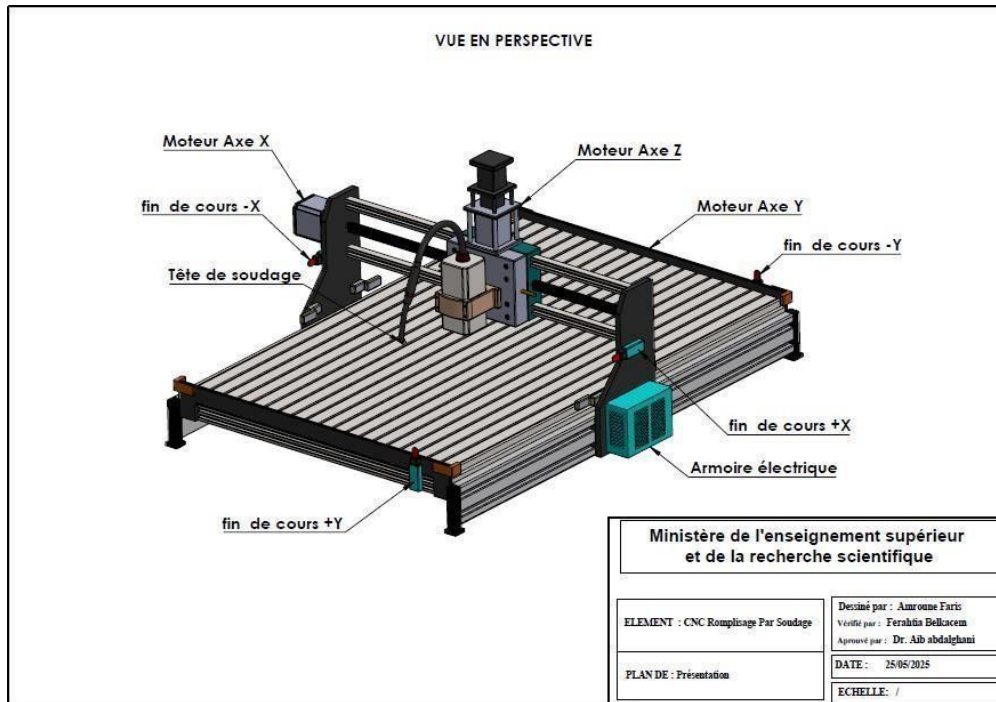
Vue en perspective de la machine CNC avec l'identification des composants principaux
